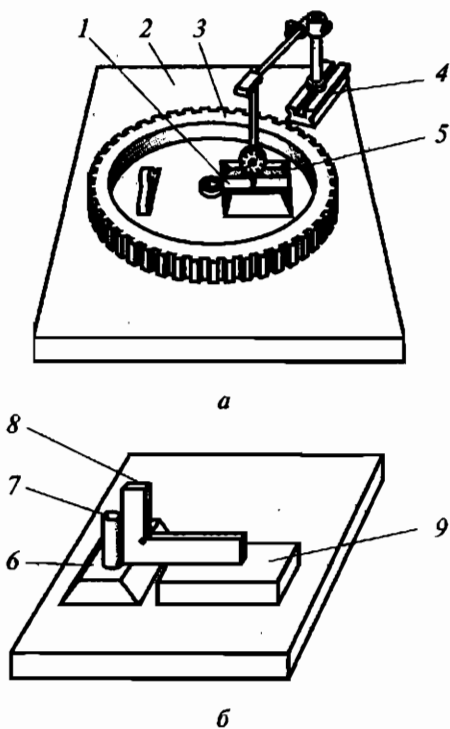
Приспособления для контроля ремонта кулисного зубчатого колеса (а) и ползушки (б):
